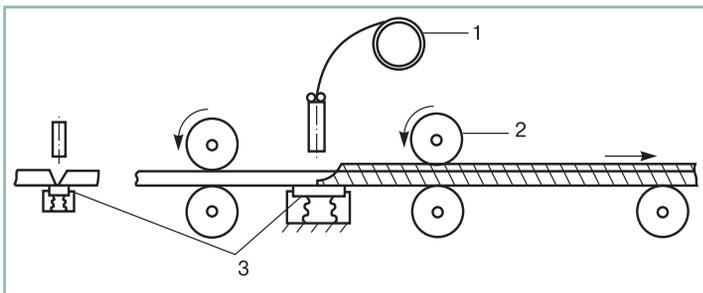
Схема односторонней автоматической сварки со стационарно закрепленным ползунком: 1 — сварочная проволока; 2 — ролики перемещения стыкуемых швов; 3 — неподвижная формирующая подкладка
